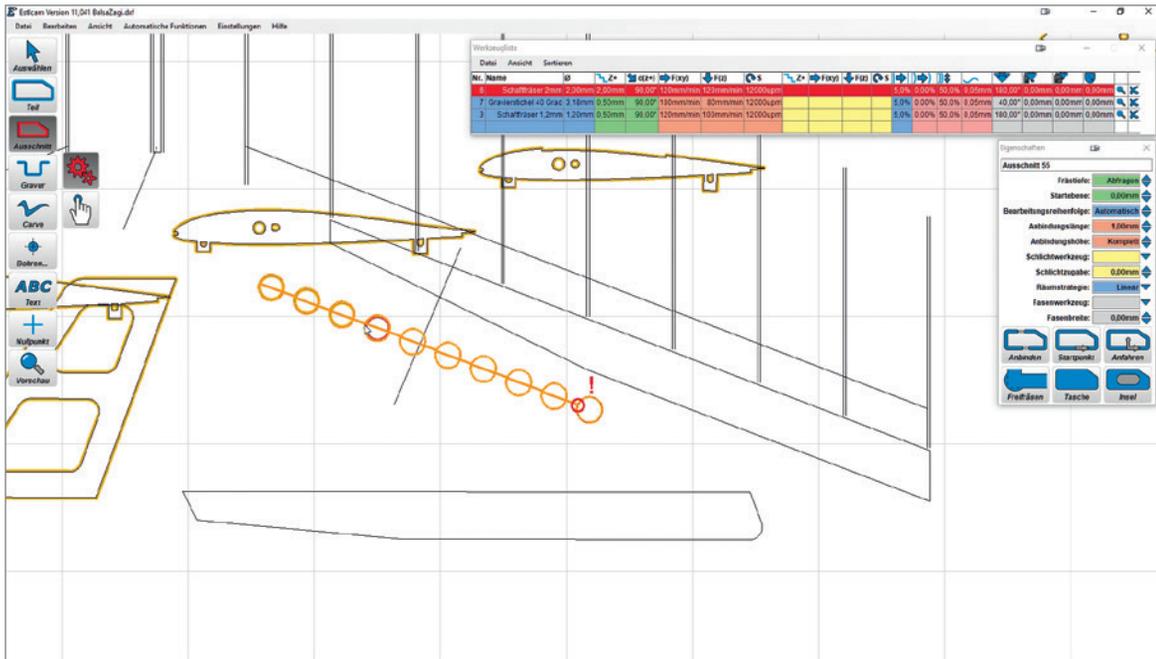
Mit etwas Geschick lässt sich sogar die zunächst unsichtbare Reihe der Erleichterungslöcher mit Fräsbahnen versehen und richtig platzieren.
